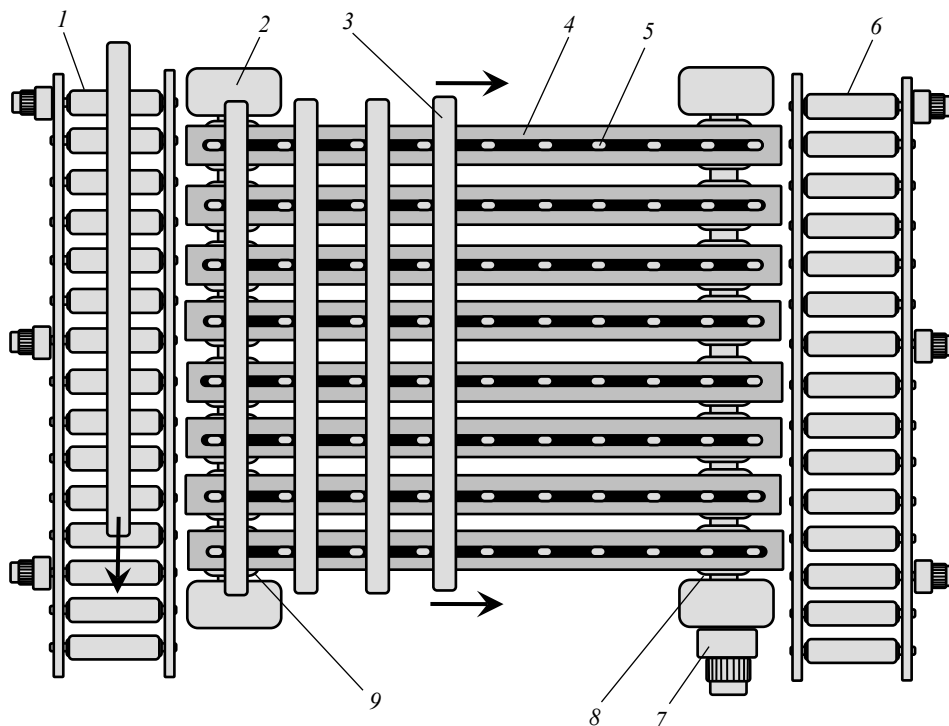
Канатний шлеппер: 1 — заготовка; 2, 6 — рольганги; 3 — підшипникова опора; 4 — стелаж; 5 — упорний палець; 7 — електродвигун; 8 — приводний барабан; 9 — натяжний блок
